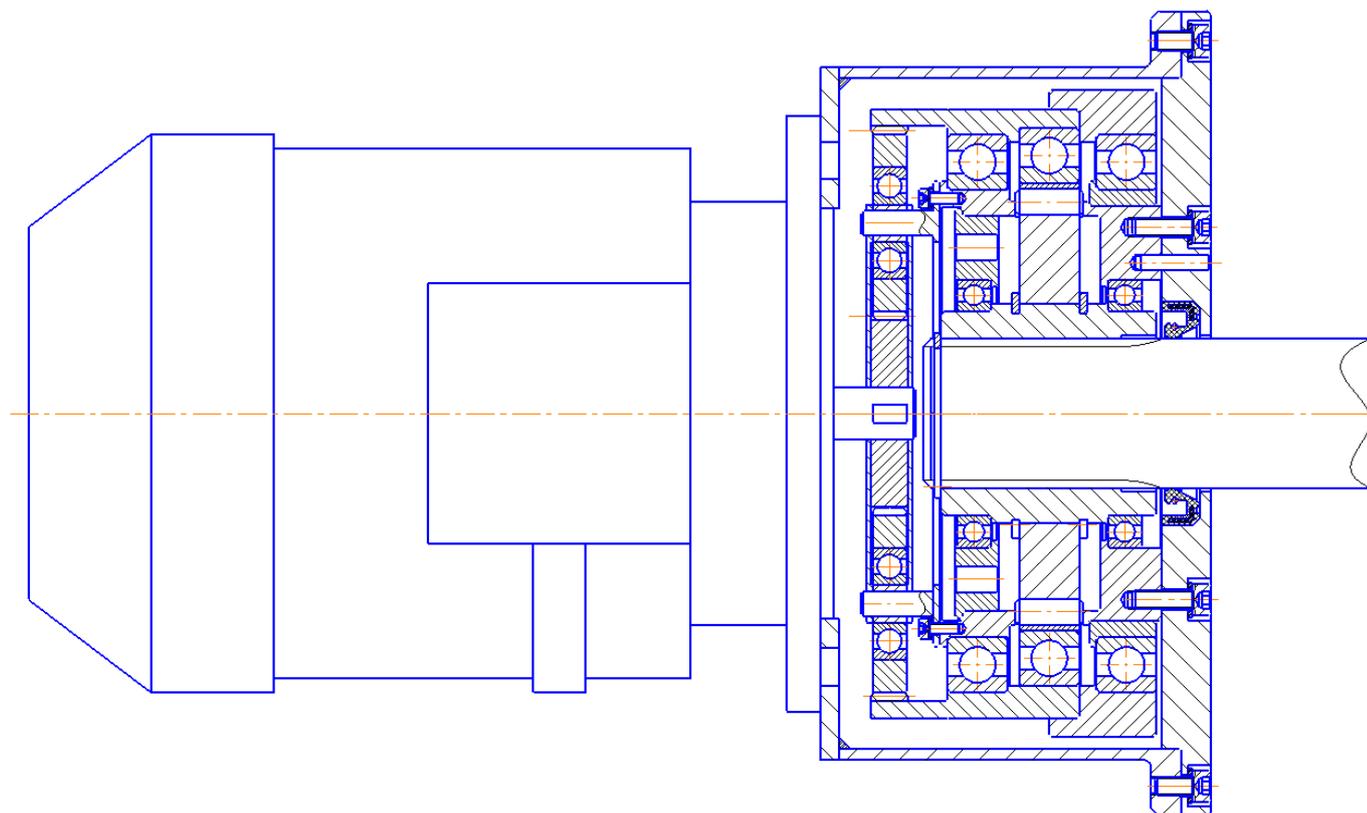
Схема привода волнового редуктора с планетарной зубчатой передачей
